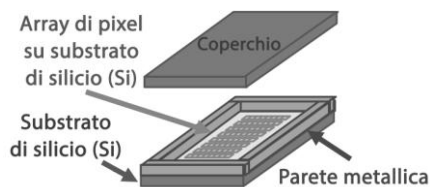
CSP (Chip-Scale Package) sotto vuoto
